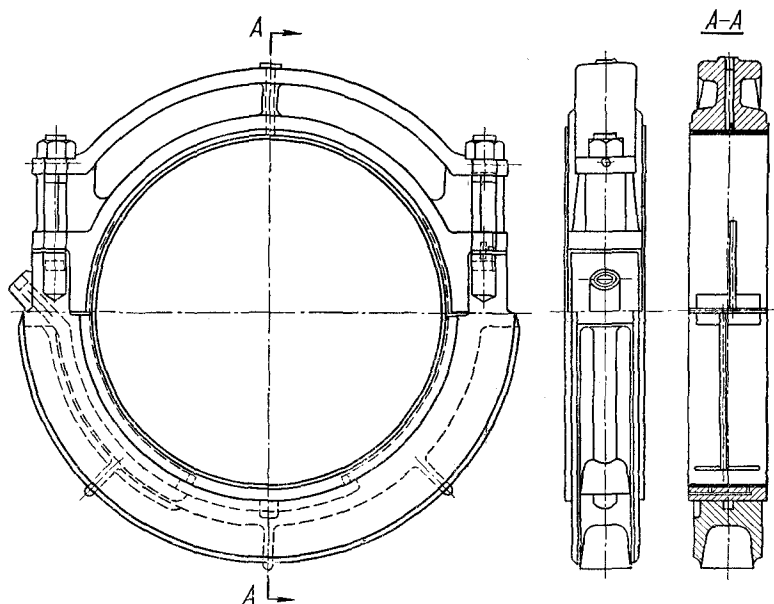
Конструкция коренного подшипника двигателя Доксфорд
